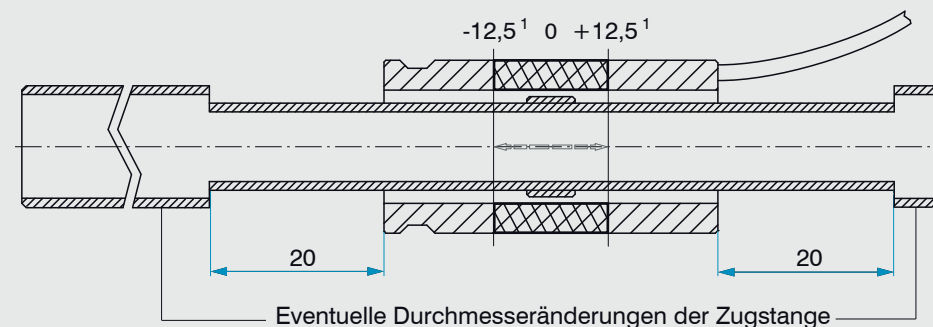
Abmessungen Zugstangenanschluss, am Beispiel LVP-25-Z20
